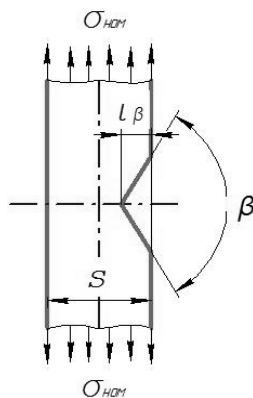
Схема сварного соединения с угловым концентратором
